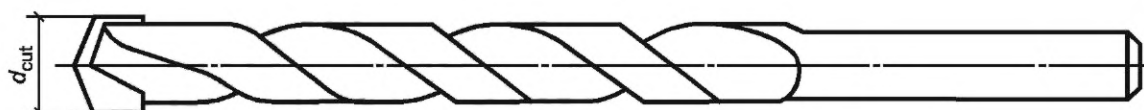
Контрольные размеры сверла для выполнения установочных отверстий под анкеры
